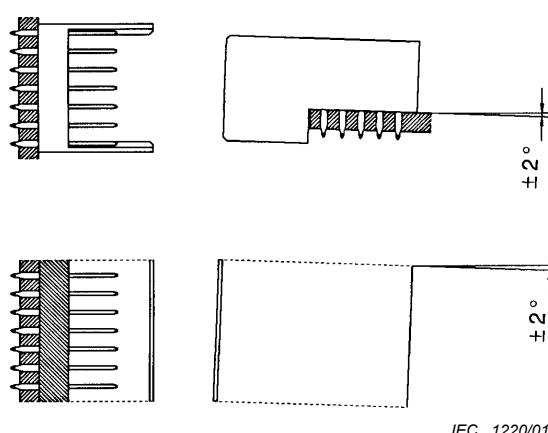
Défauts d'inclinaison suivant les axes longitudinal et transversal
